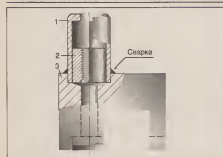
Сварка втулки ключа с корпусом:
